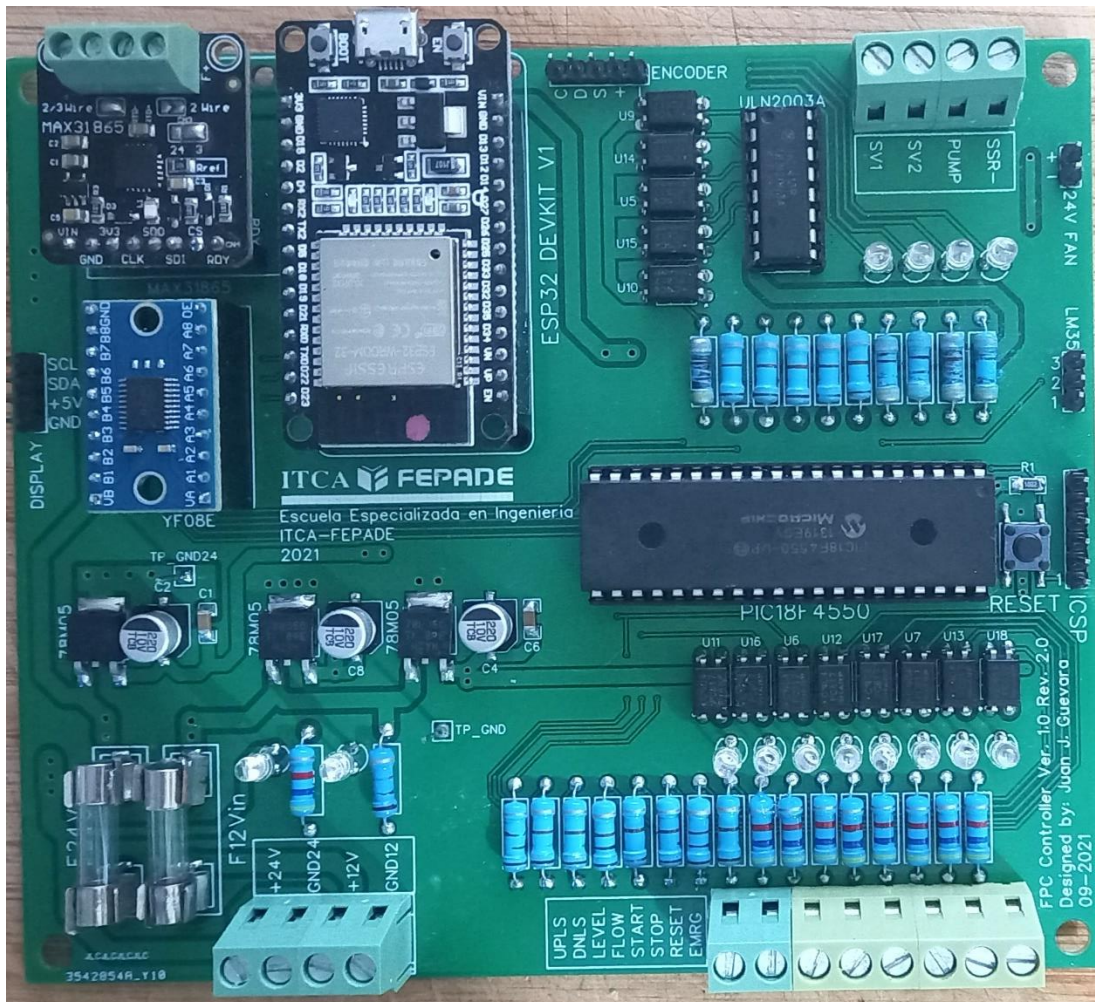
Tarjeta PCB del controlador electrónico con dispositivos electrónicos soldados.
